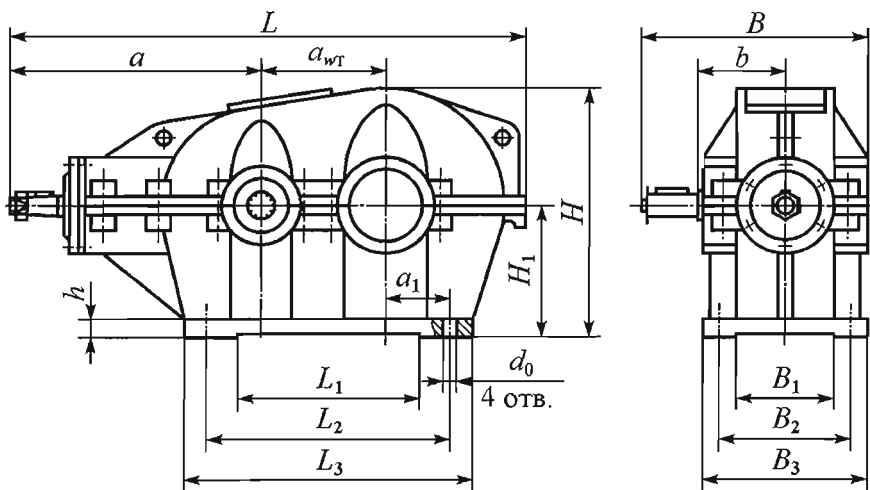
Габаритные, установочные и присоединительные размеры редуктора
